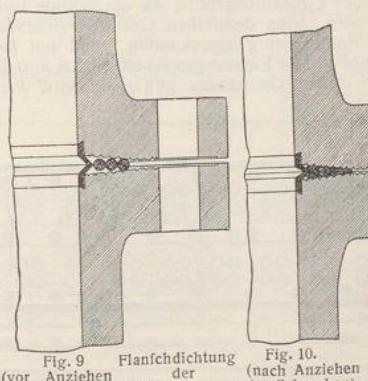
Flanschdichtung der Gebr. Böhmer (vor Anziehen der Schrauben).
